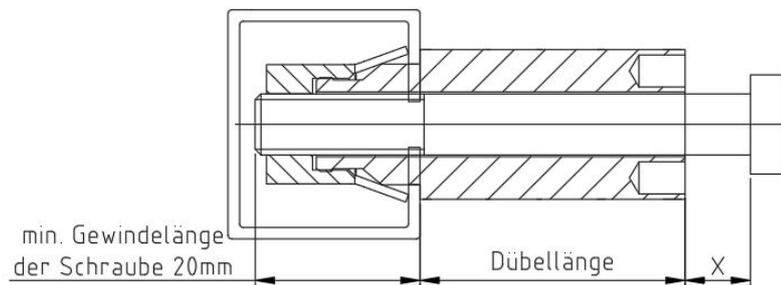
Vorgaben zur Schraubenlänge und Gewindelänge
